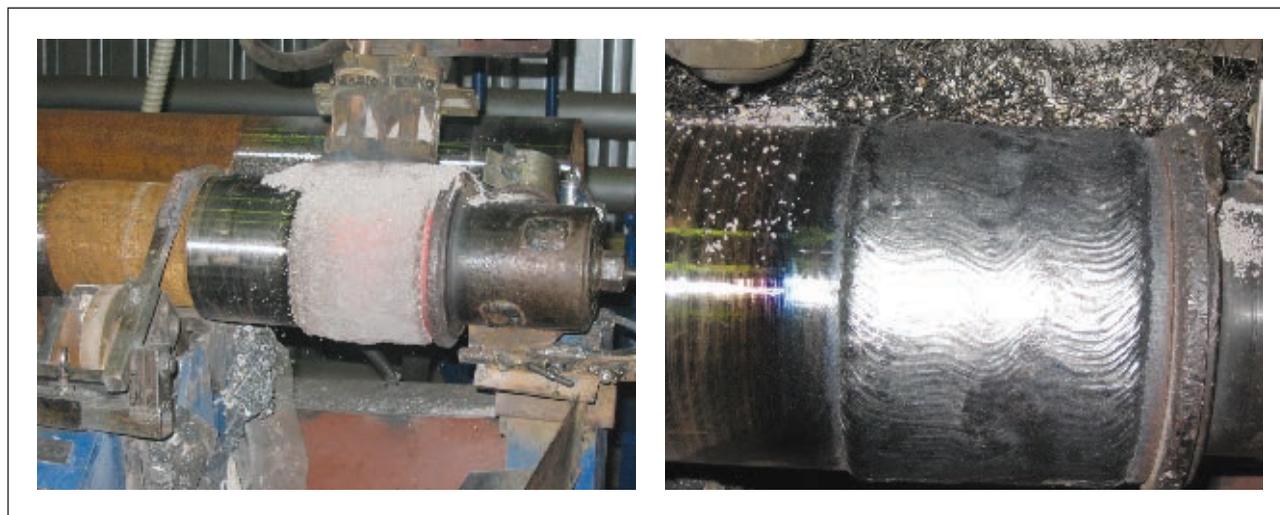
Наплавка изношенной поверхности цилиндрических деталей
